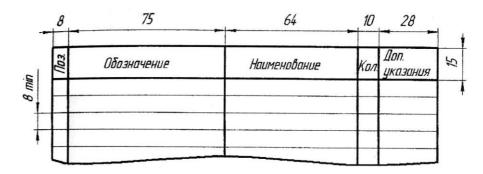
Форма таблицы составных частей изделия чертежа общего вида
